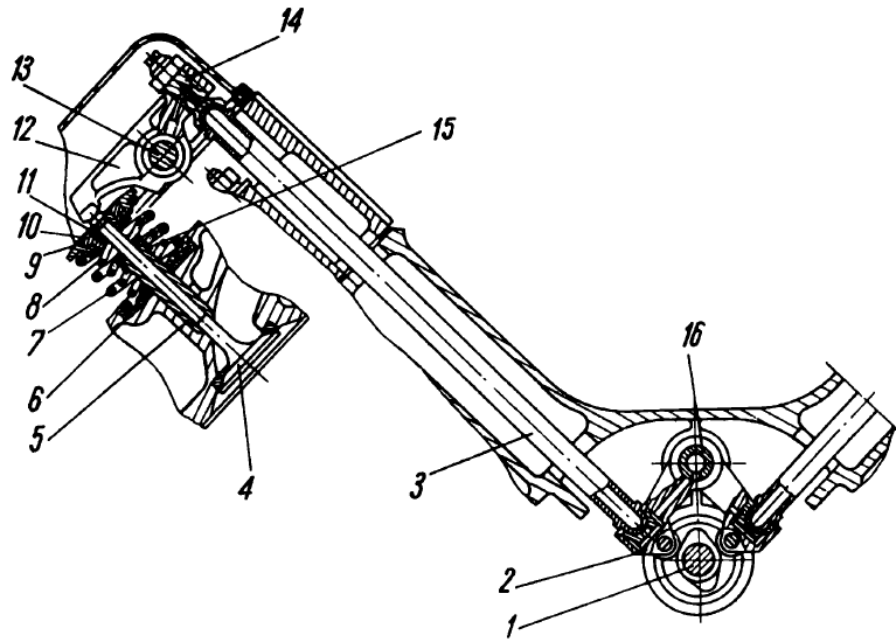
Механізм газорозподілу: 1 – розподільний вал; 2 – штовхач; 3 – штанга штовхача; 4 – клапан; 5 – напрямна втулка; 6 – шайба пружин клапана; 7 – зовнішня пружина; 8 – внутрішня пружина; 9 – тарілка пружин клапана; 10 – втулка тарілки пружин клапана; 11 – сухар; 12 – коромисло; 13 – вісь коромисел; 14 – регулювальний гвинт; 15 – прокладка манжета; 16 – вісь штовхачів
